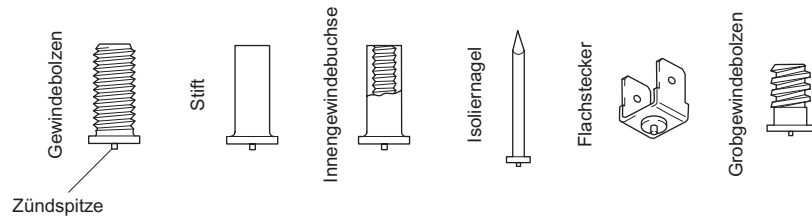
6 Einige Beispiele verschiedener Ausführungen von Schweißelementen mit Zündspitze
